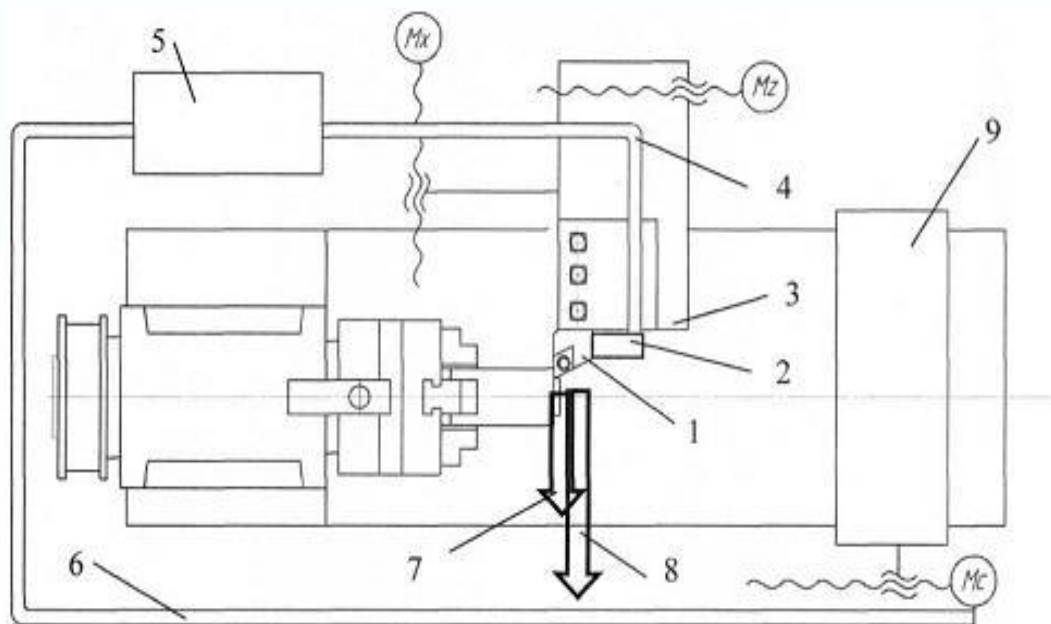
Схема технологічної системи оброблення з динамічним керуванням коливаннями супорта токарного верстата
